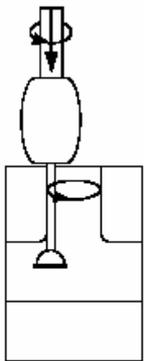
Das Werkzeug ins Zentrum der Bohrung führen.
